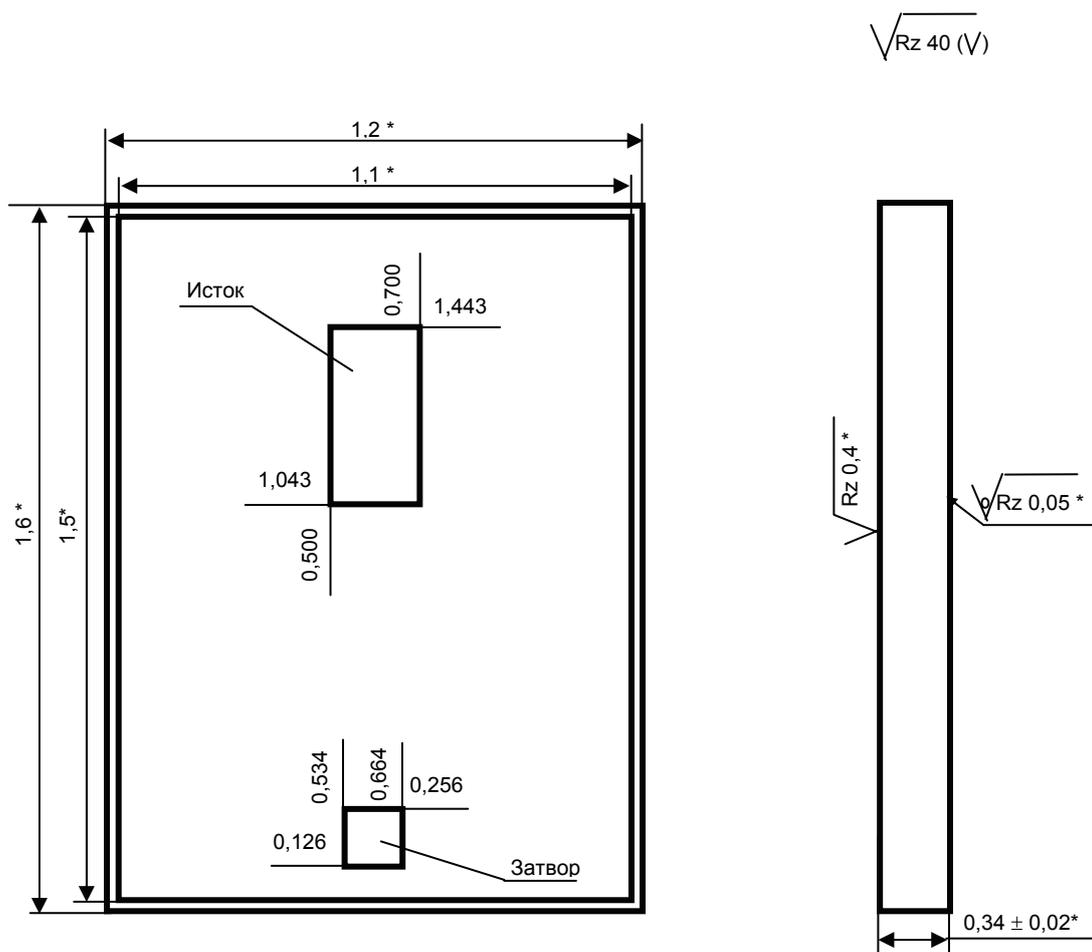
Габаритный чертеж кристалла 2P524A-5
